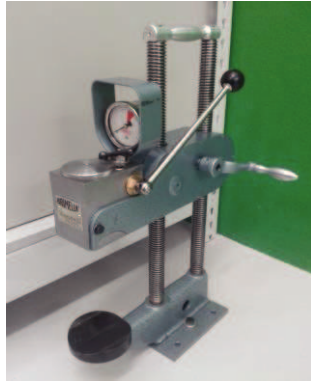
Equipamento de dureza Brinella HBW 3000, Mecadrum
